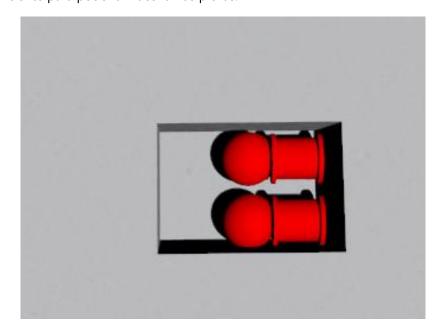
Detalle de cavidad para almacenaje de piezas
